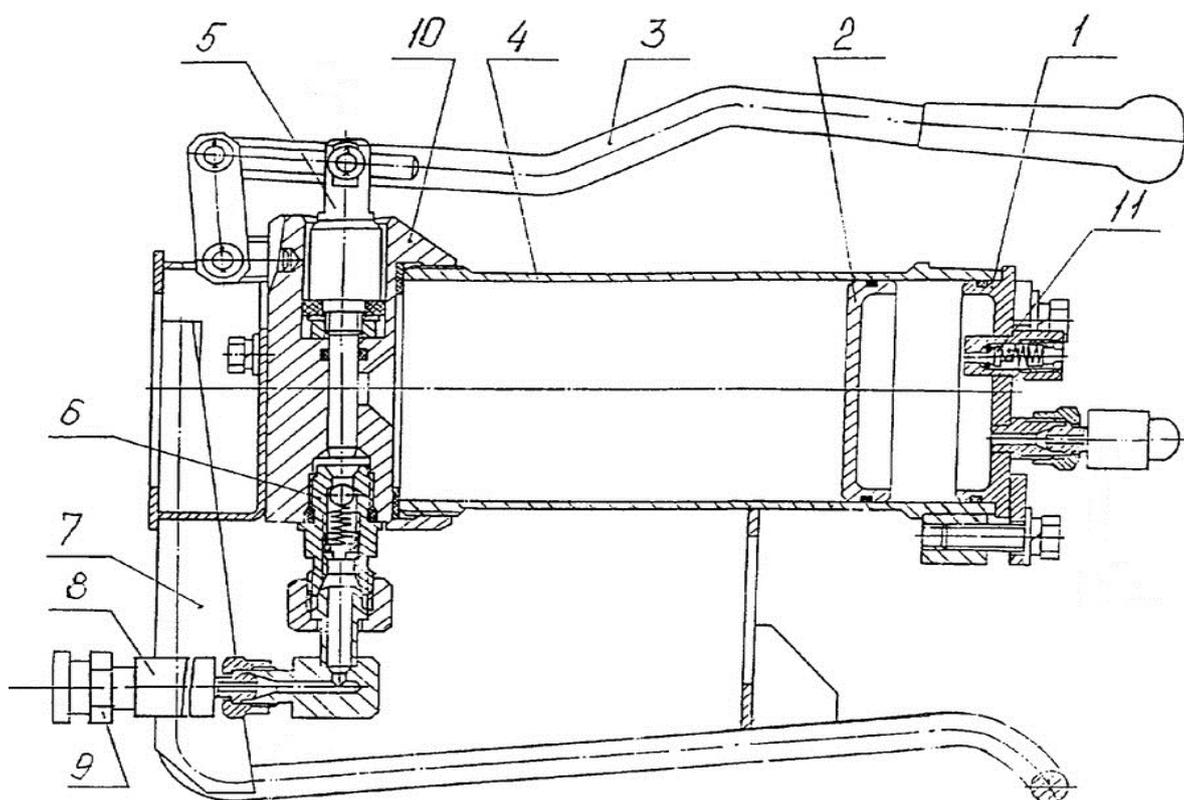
патент РФ № 2332611 устройство для подачи смазки.
